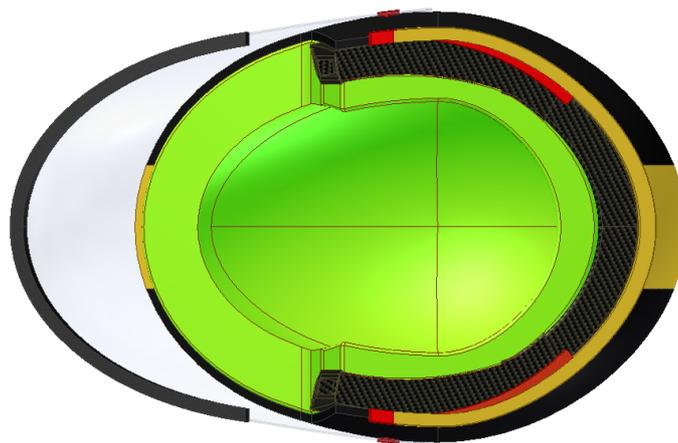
Sistema sensorial instalado en la parte inferior de la caja y las barras de sistema estructural de protección
